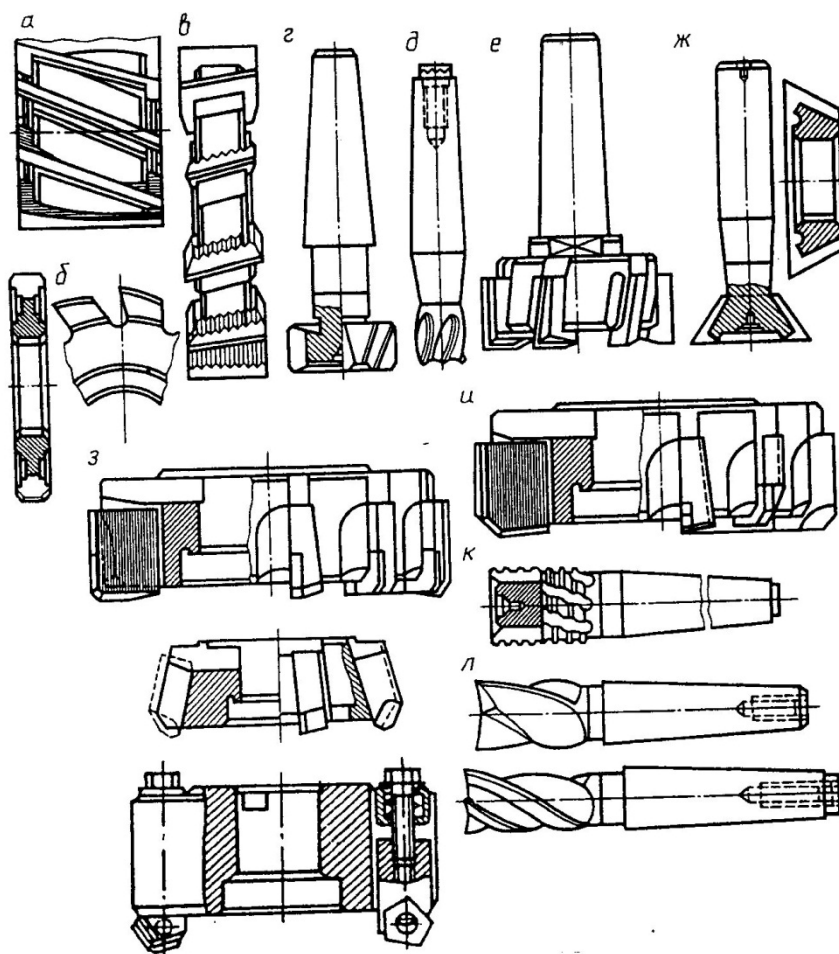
Типы фрез: а – цилиндрическая; б, в – дисковые; г – Т-образная; д – концевая; е – торцевая с хвостовиком; ж – угловые концевая и насадная; з – торцовые насадные; со вставными ножами и механическим креплением пятигранных пластин; и – торцовая ступенчатая; к – концевая обдирочная; л – концевые шпоночные
